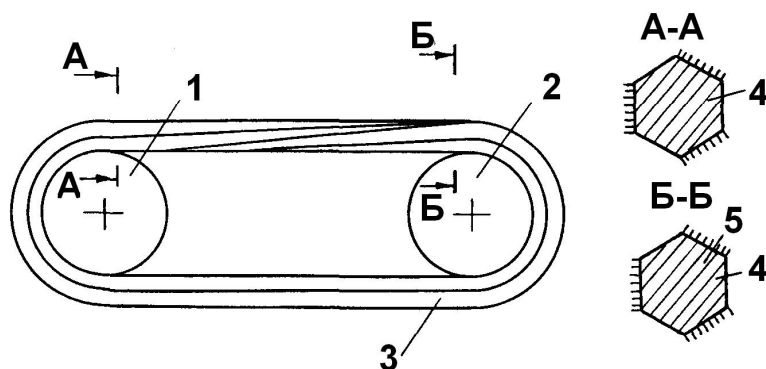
Гибкий кольцевой шлифовальный ремень
